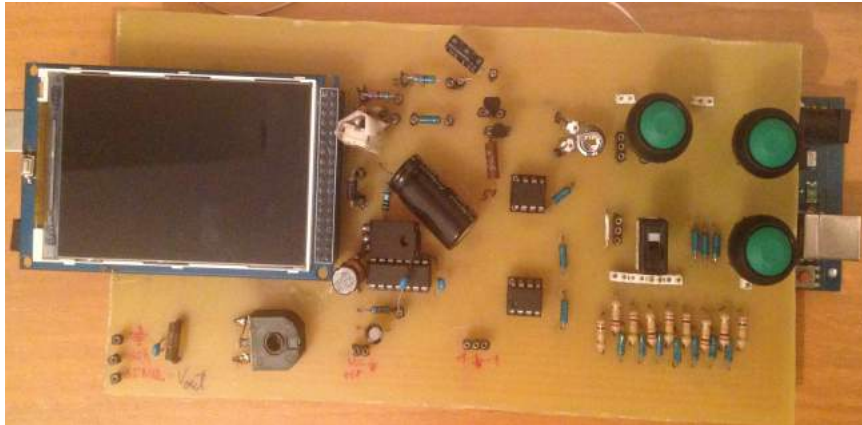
Imagem da placa PCB com os componentes eletrônicos soldados.
